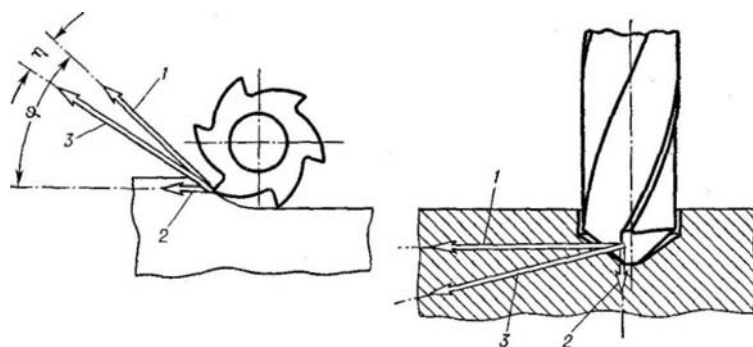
Направления движений (слева — при фрезеровании, справа — при сверлении):
